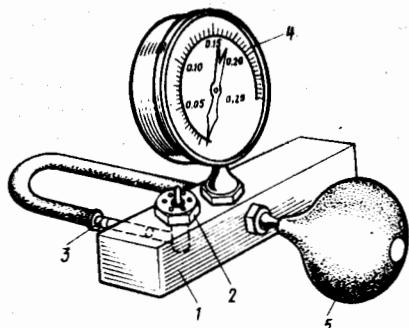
Прибор для проверки герметичности игольчатого клапана поплавковой камеры:
